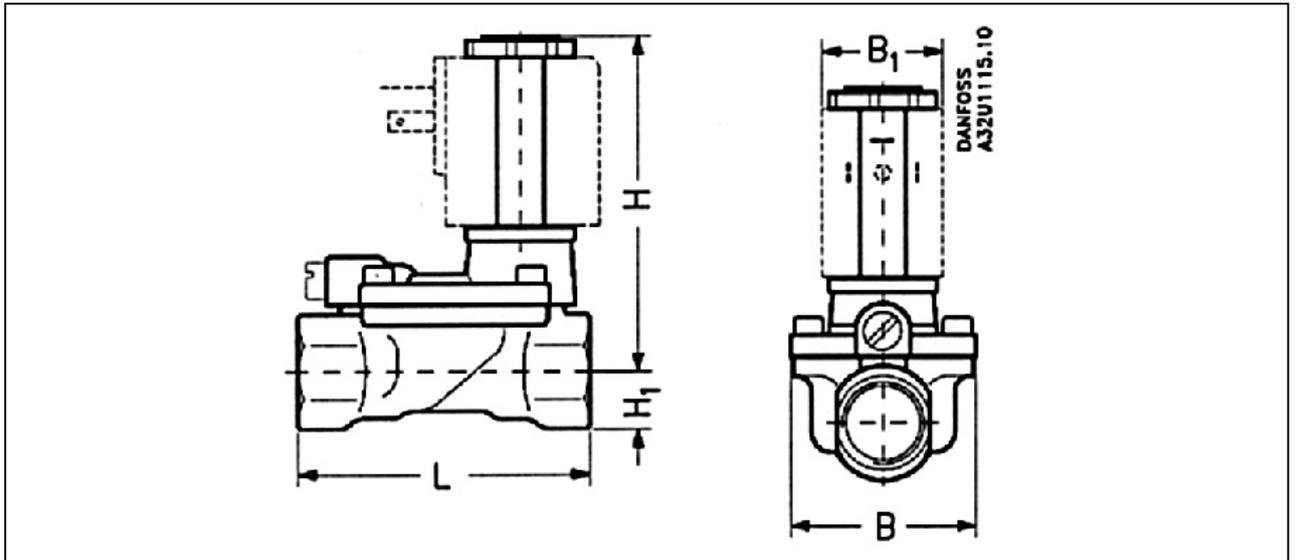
Габаритные и присоединительные размеры соленоидного клапана.
